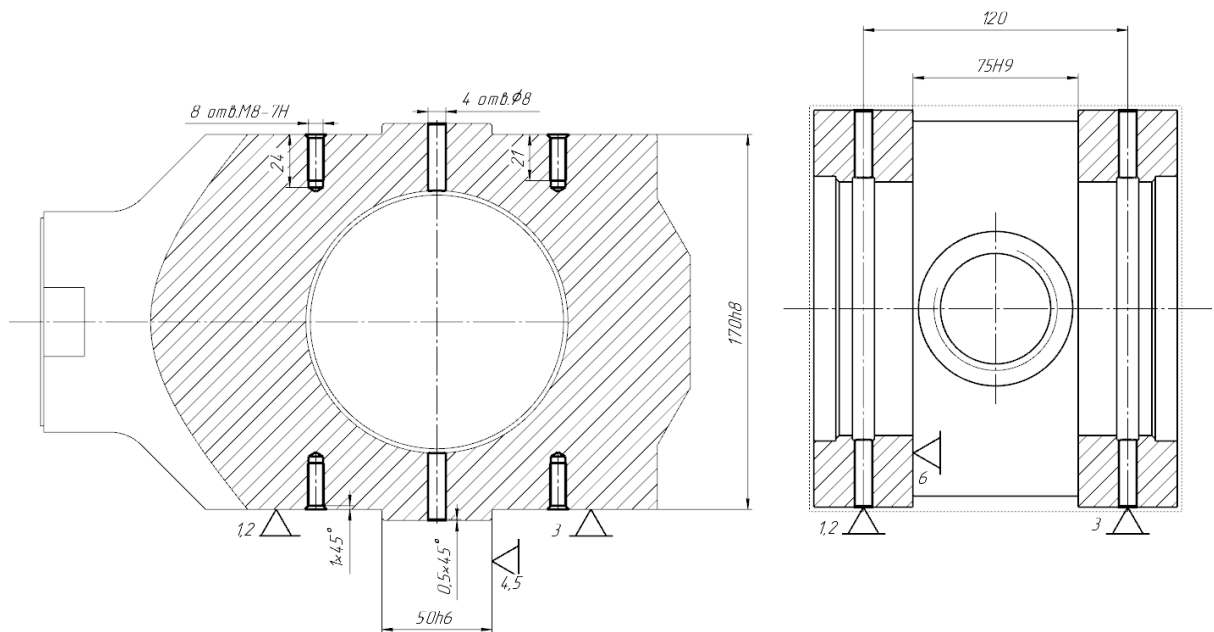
Схема базування на операції «260 Свердлильна»
